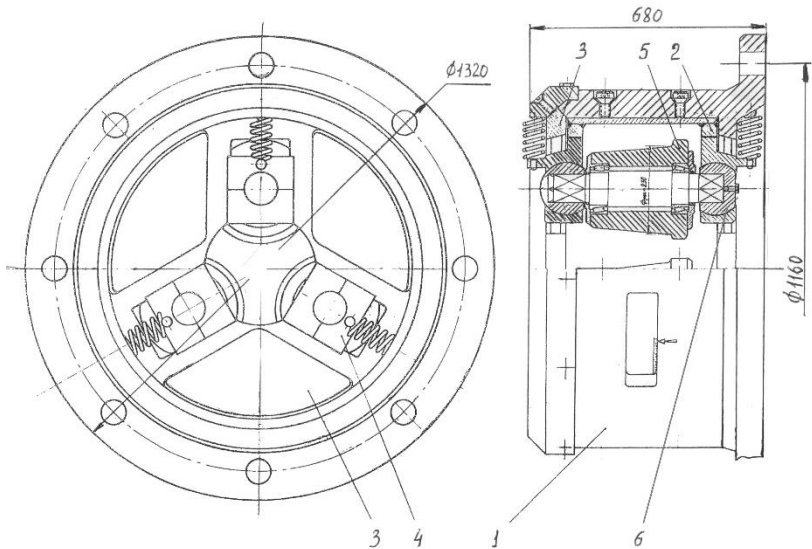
Загальний вид роликів кассети: 1 – корпус кассети; 2 – кулачковий натискний пристрій для радіального переміщення опор ролика; 3 – поворотна планшайба; 4 – роликів вузол; 5 – ролик; 6 – сферичні подушки опор роликів.
